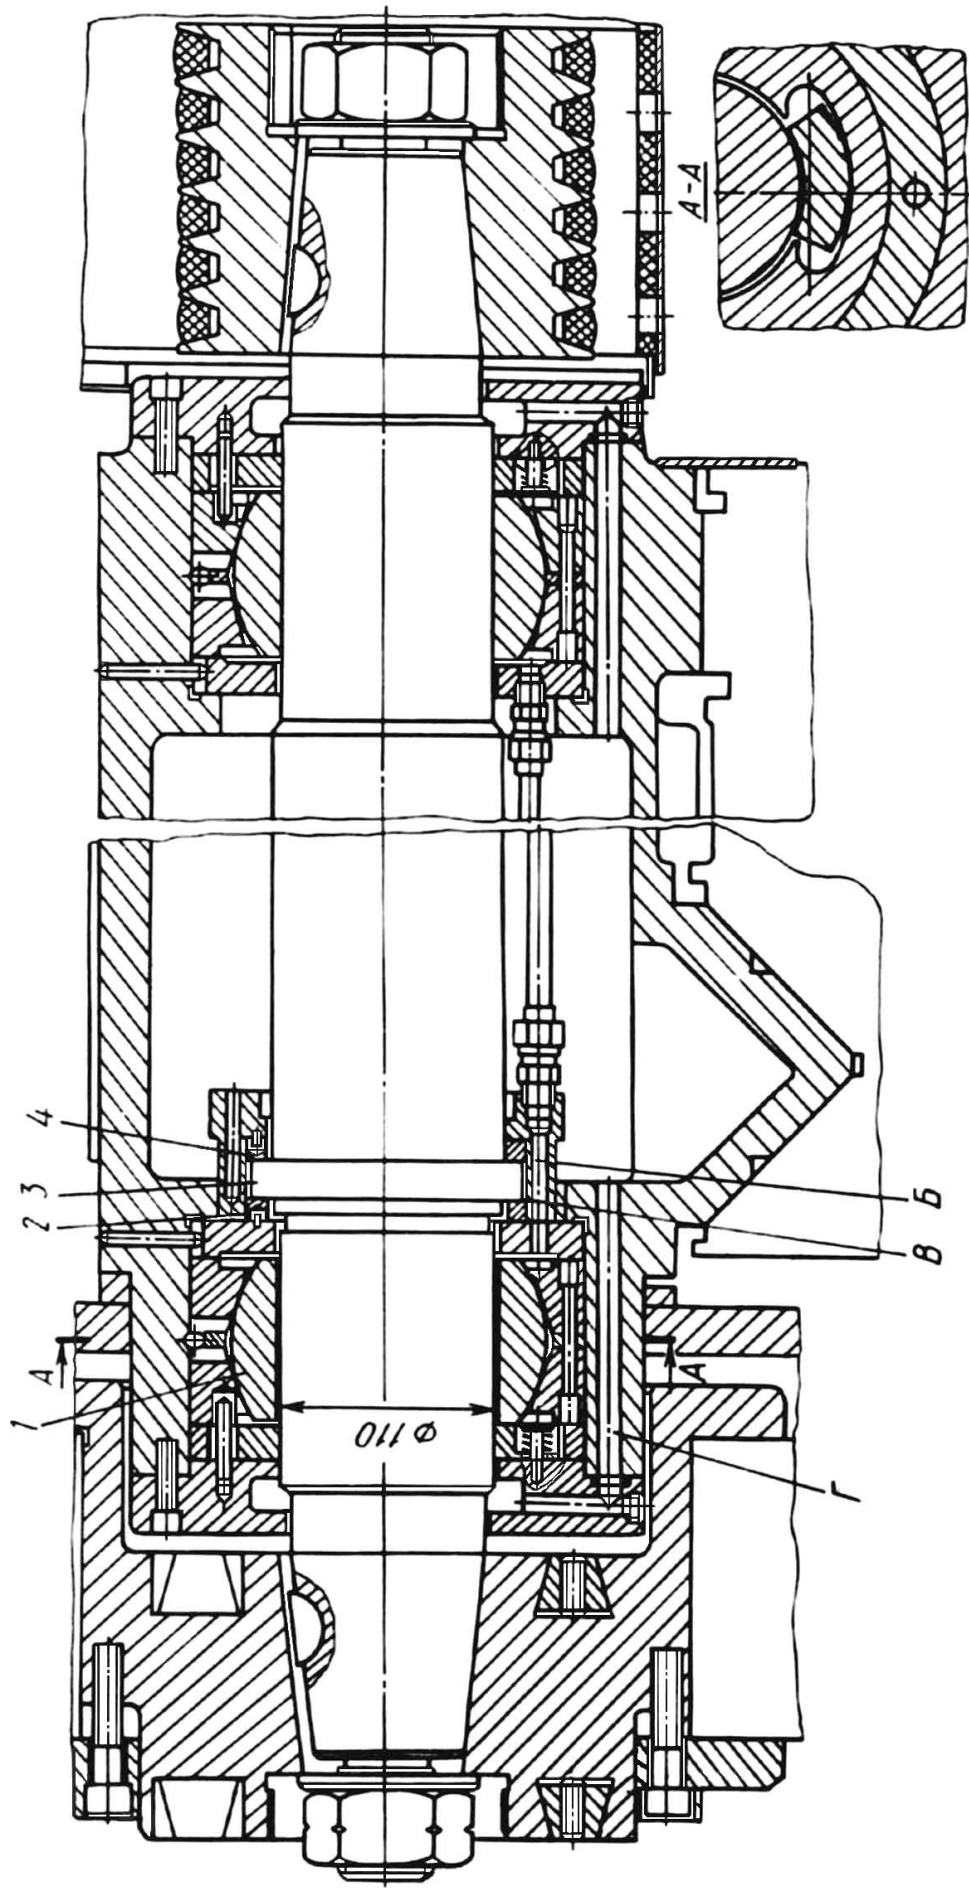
Шпиндельный узел шлифовального верстака с гидродинамичными опорами
